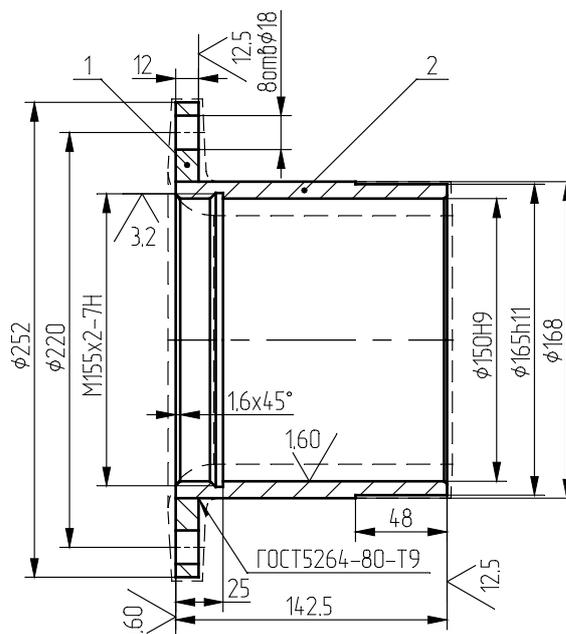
Чертеж детали перехода: 1 – плоский фланец, 2 – втулка.
